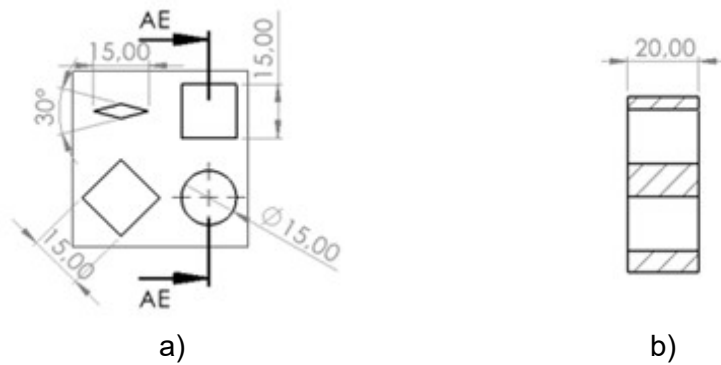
Geometría de los agujeros (a) Planta (b) Perfil.
